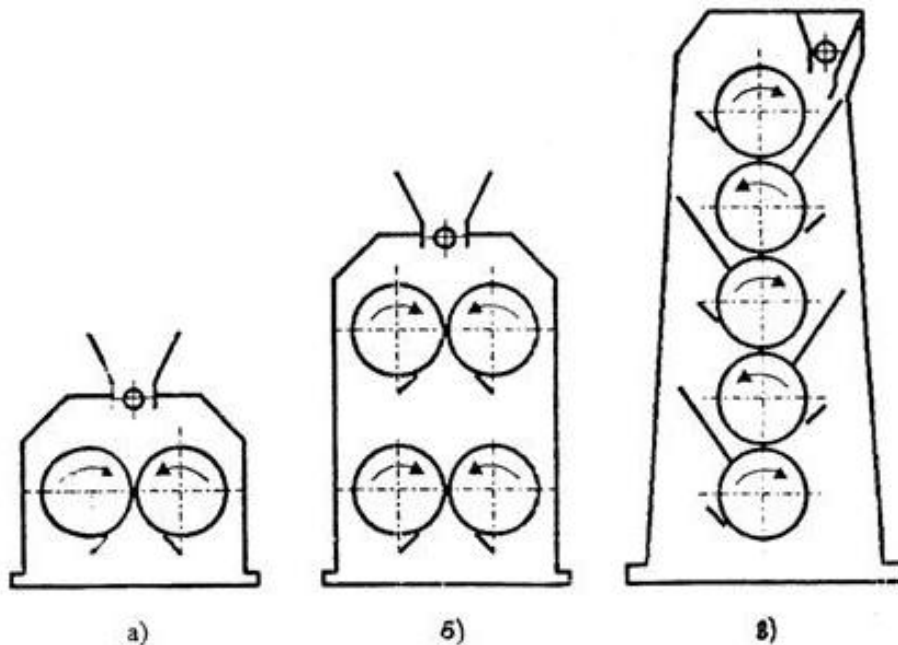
Схеми конструкцій вальцевих верстатів: а) – однопарний; б) – двопарний; в) – п'ятивальцевий
